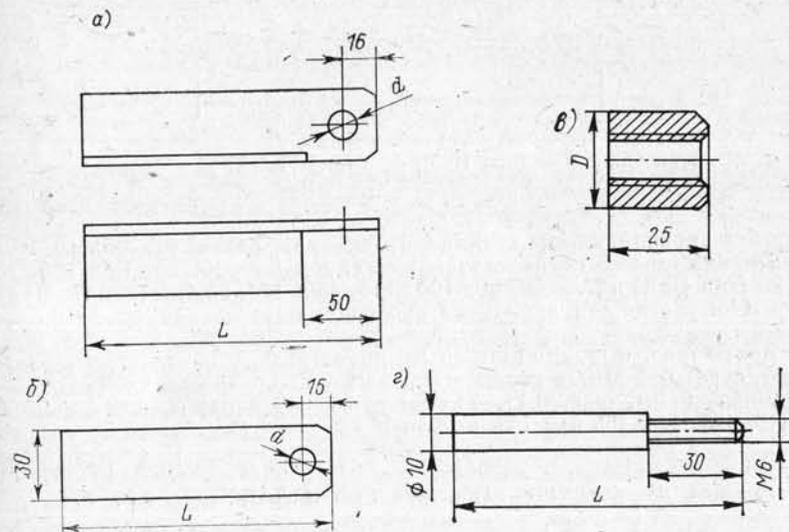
Детали для заземления корпусов электрооборудования: *a* — стойка; *б* — планка; *в* — бонка; *г* — шпилька.
